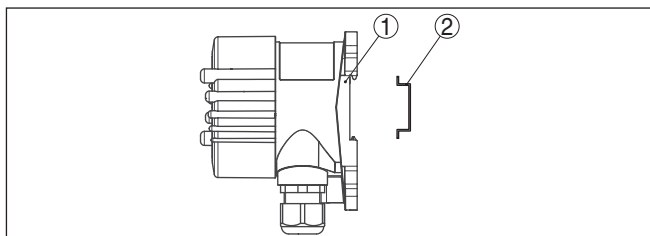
VEGADIS 82 с пластиковым корпусом для монтажа на несущей рейке
